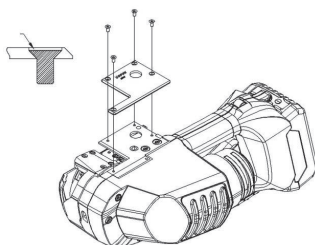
ILLUSTRAZIONE DEL MONTAGGIO DELLA PIASTRA RESISTENTE ALL'USURA
